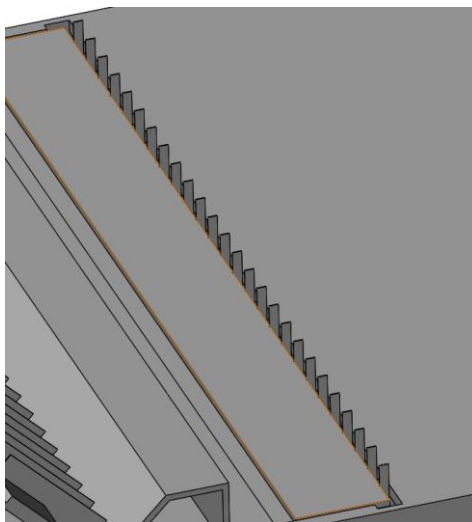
Chapas para separar as molas para soldar a parte inferior do linguete
